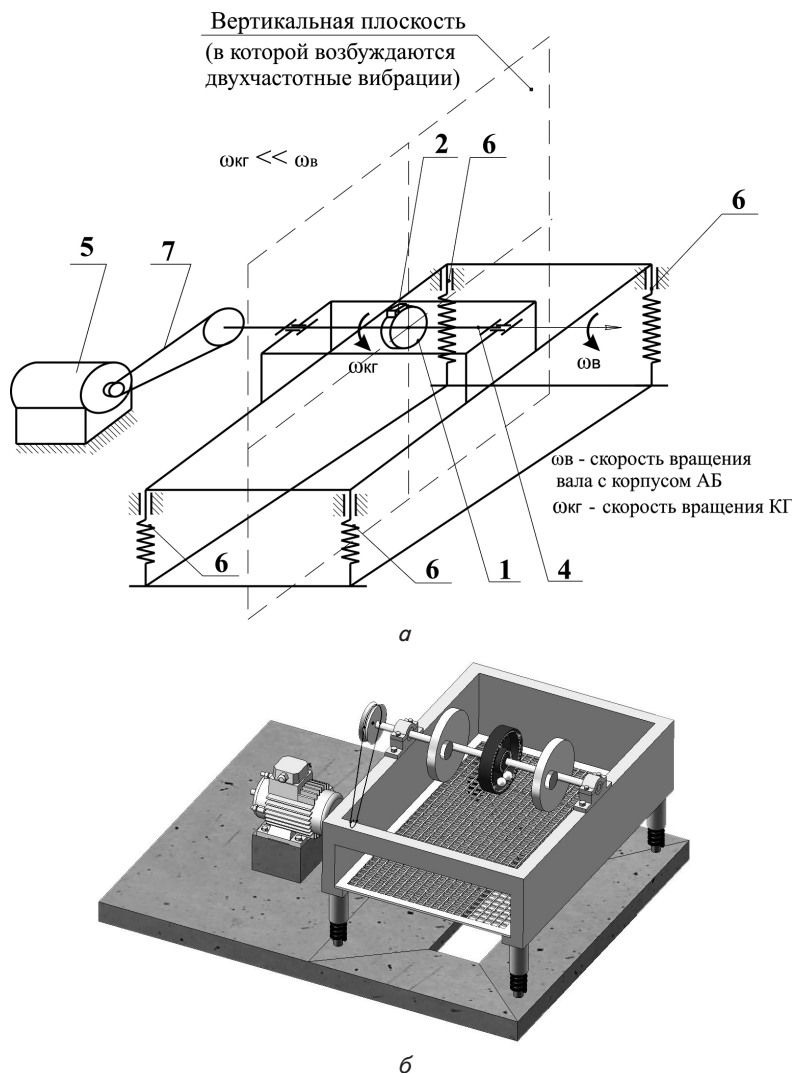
Модель вибрационной машины: а – механическая; б – 3D модель: 1 – корпус АБ; 2 – дебаланс; 4 – вал; 5 – электродвигатель; 6 – опора; 7 – ременная передача
